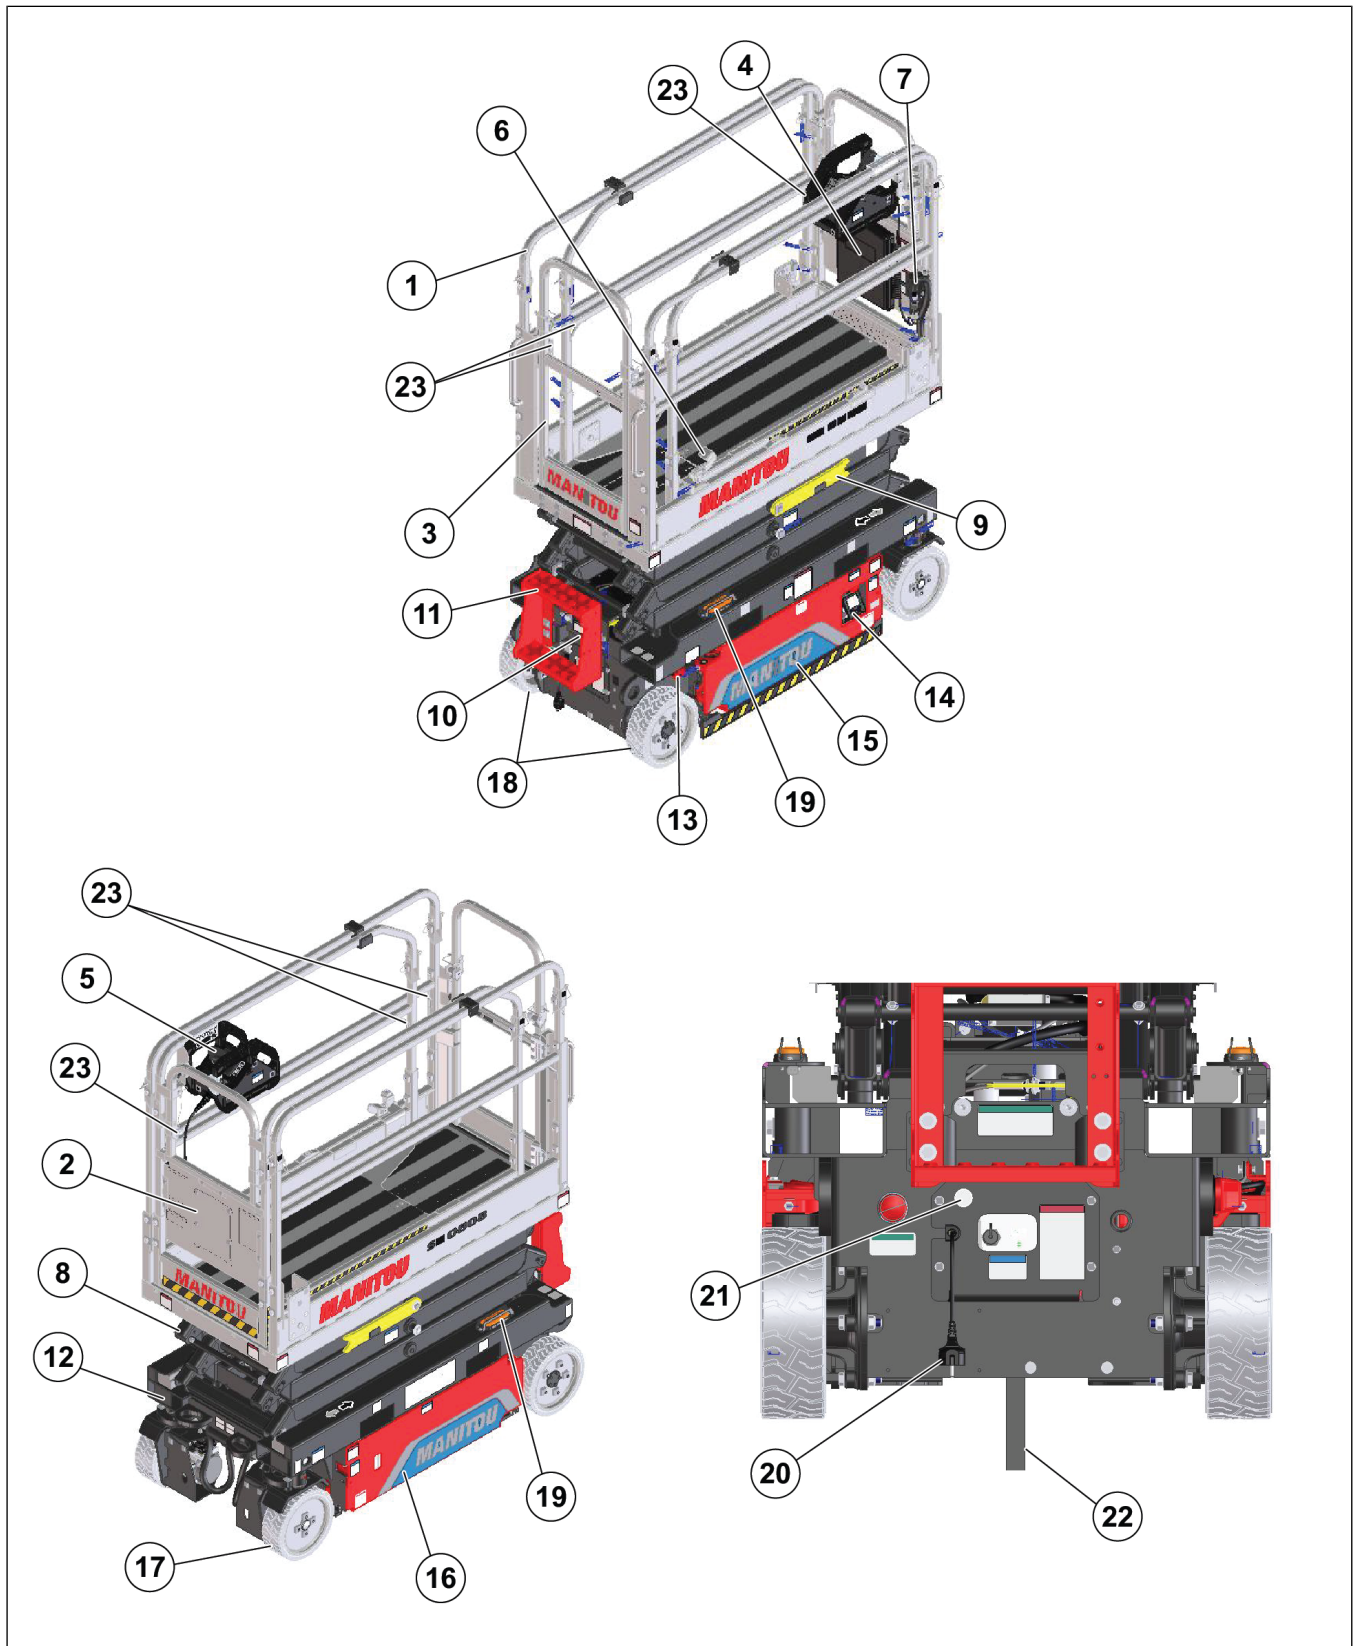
Emplacement des composants de la machine - SE 0808 24V S1
